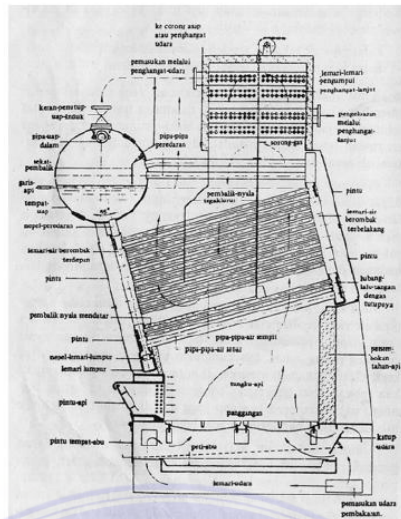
Ketel Pipa Air (water tube boiler).
